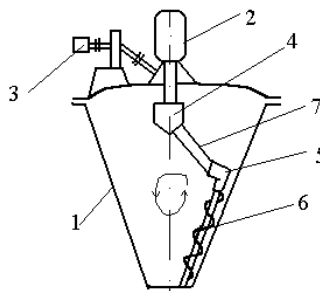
Планетарно-шнековый смеситель с вращающимся конусом: 1 - корпус; 2 - привод шнека 6; 3 - привод водила 7; 4, 5 - косозубые передачи
